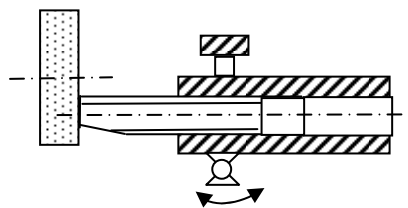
Заточка торцовых режущих кромок в приспособлении
